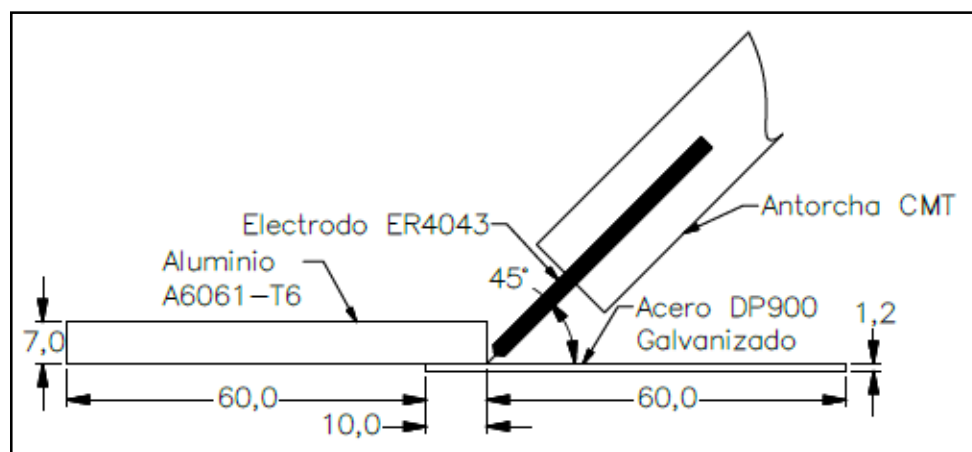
Configuración de unión disímil A6061-T6/DP900 galvanizado con proceso CMT
